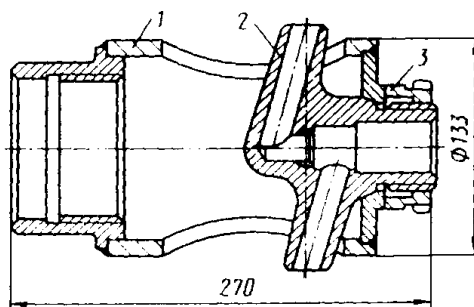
Приспособление для проточки уплотнительных поверхностей корпусов вентилях с D_y 10—20 мм:
